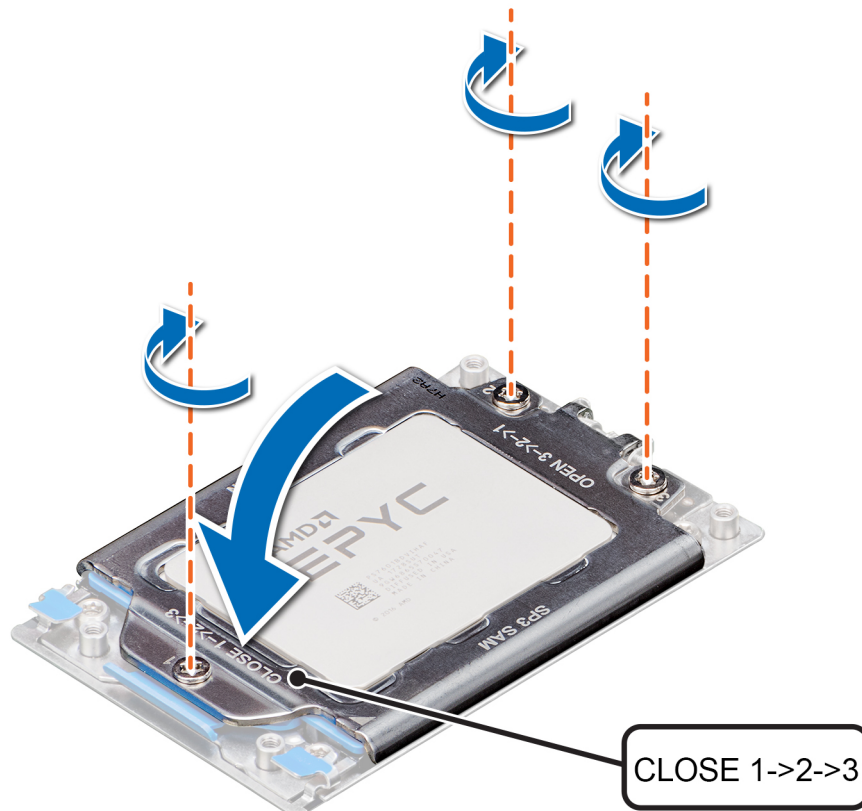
Fijación de la cubierta del zócalo del procesador
